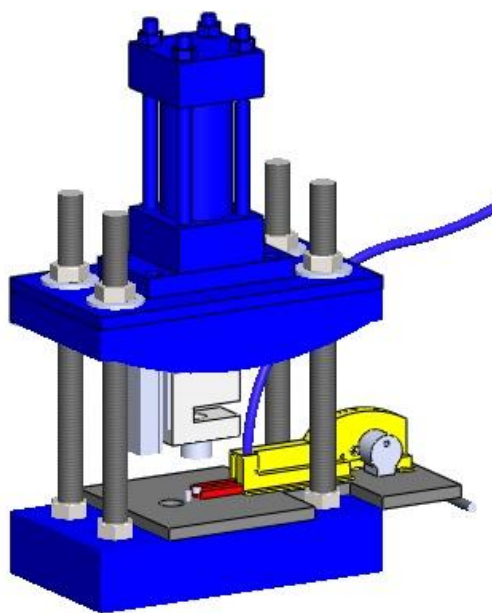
Estrutura de compressão da Máquina de Ensaio de compressão Didática remota (MDTEC)
